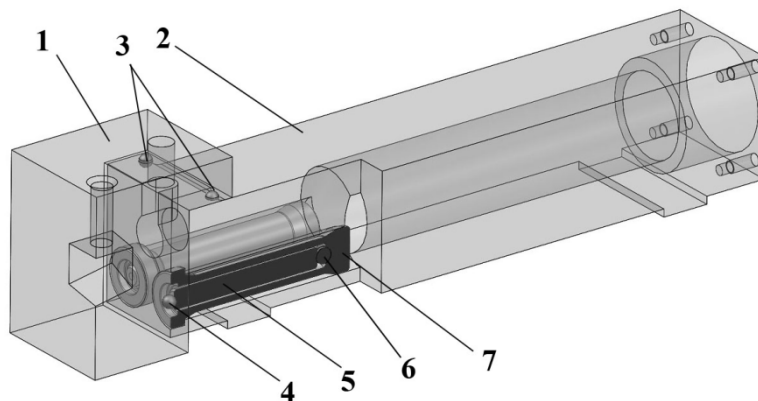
Конструкция РИТ-С2: 1 – головка; 2 – корпус (державка); 3 – опорные шарики; 4 – упорный шарик; 5 – стержень мездозы; 6 – шаровая опора; 7 – стакан
